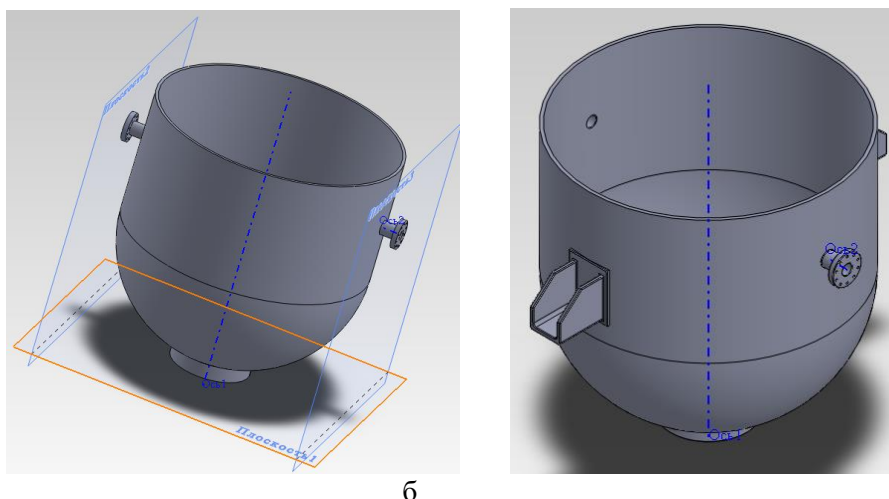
а) корпус реактора; б) фланцевое соединение на корпусе
